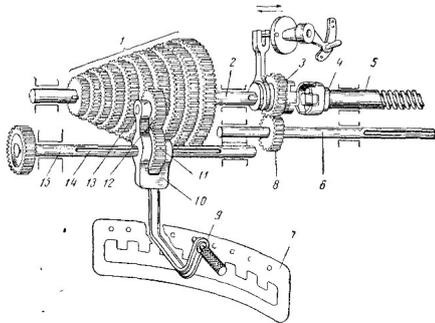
Схема коробки подач с подвижными зубчатыми колесами
